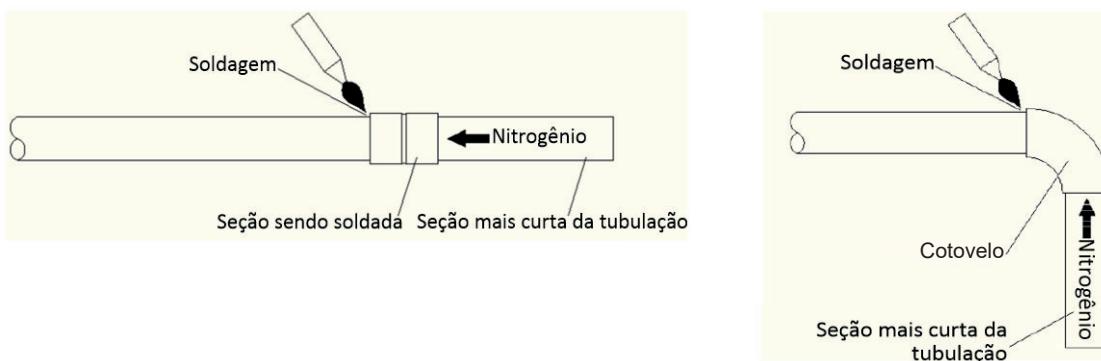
Fluxo de nitrogênio pela tubulação durante a soldagem
